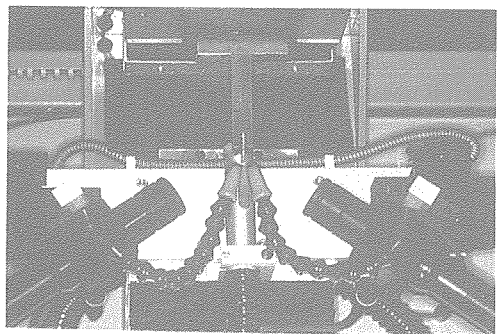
Laser canon과 video camera로 구성된 Procera laser welding system
